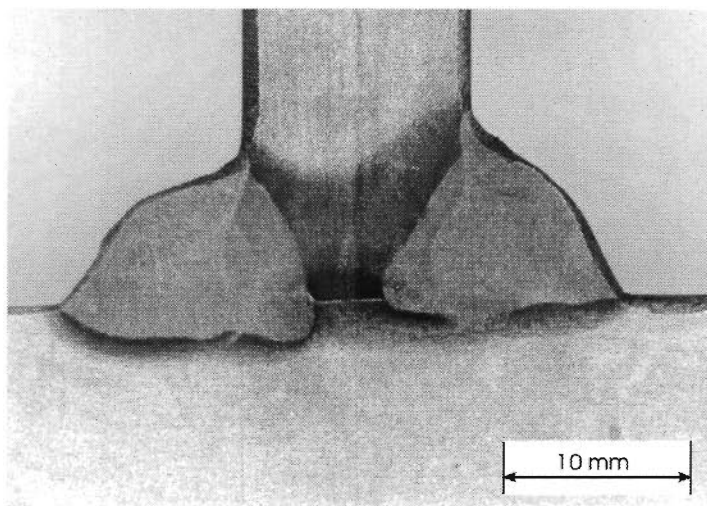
Feinschliff des Probekörpers im Schweißnahtbereich, Stirnplatte $t = 30 \text{ mm}$
